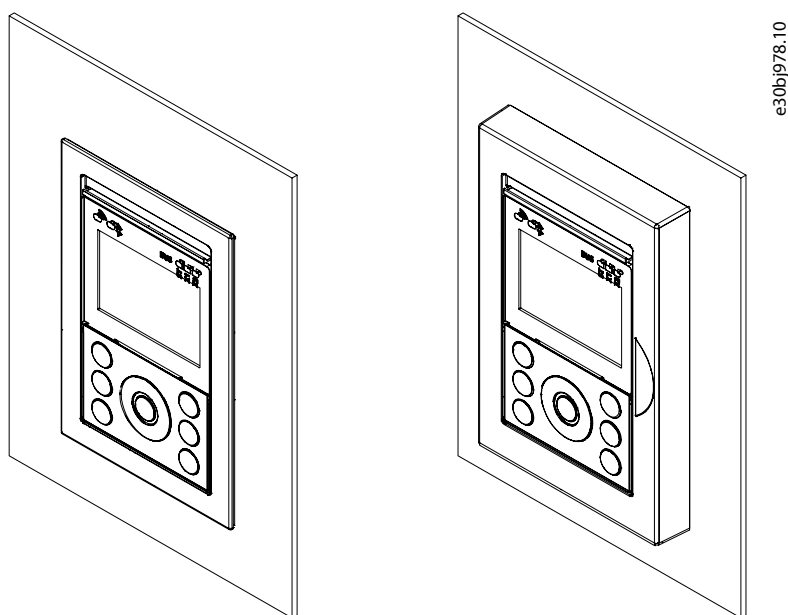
Panel de control montado en kit de montaje empotrado (izquierda) y kit de montaje en superficie (derecha)
